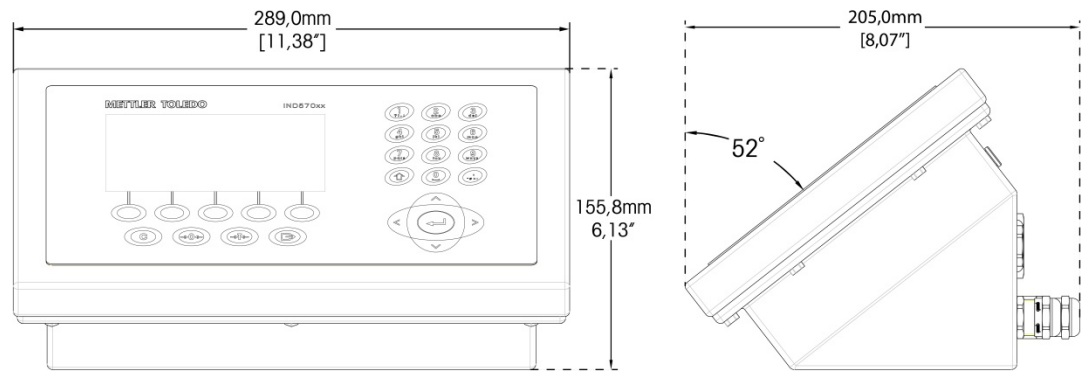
Dimensiones de la caja para ambientes adversos del IND570xx
